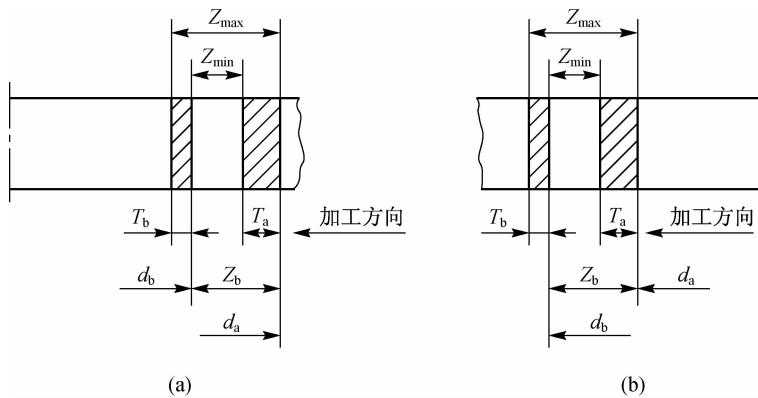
被包容件的工序加工余量和工序尺寸公差
